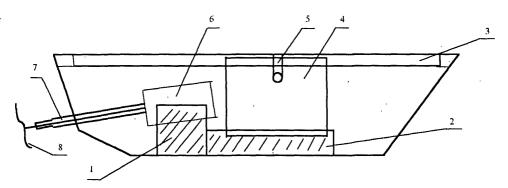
Вид сбоку: 1 — крепежная рейка двигателя; 2 — крепежная рейка редуктора; 3 — палубная крепежная рейка; 4 — редуктор; 5 — отверстие под выходной вал редуктора; 6 — двигатель хода; 7 — кожух вала гребного винта; 8 — гребной винт
